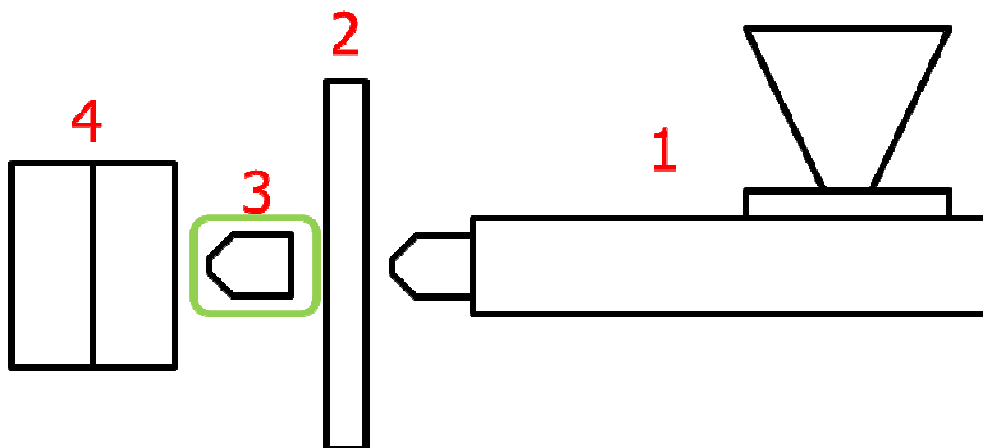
Schematischer Aufbau der eingesetzten Spritzgießmaschine; (1) Spritzzylinder, (2) Umschaltplatte, (3) Düse, (4) Werkzeug [115]
